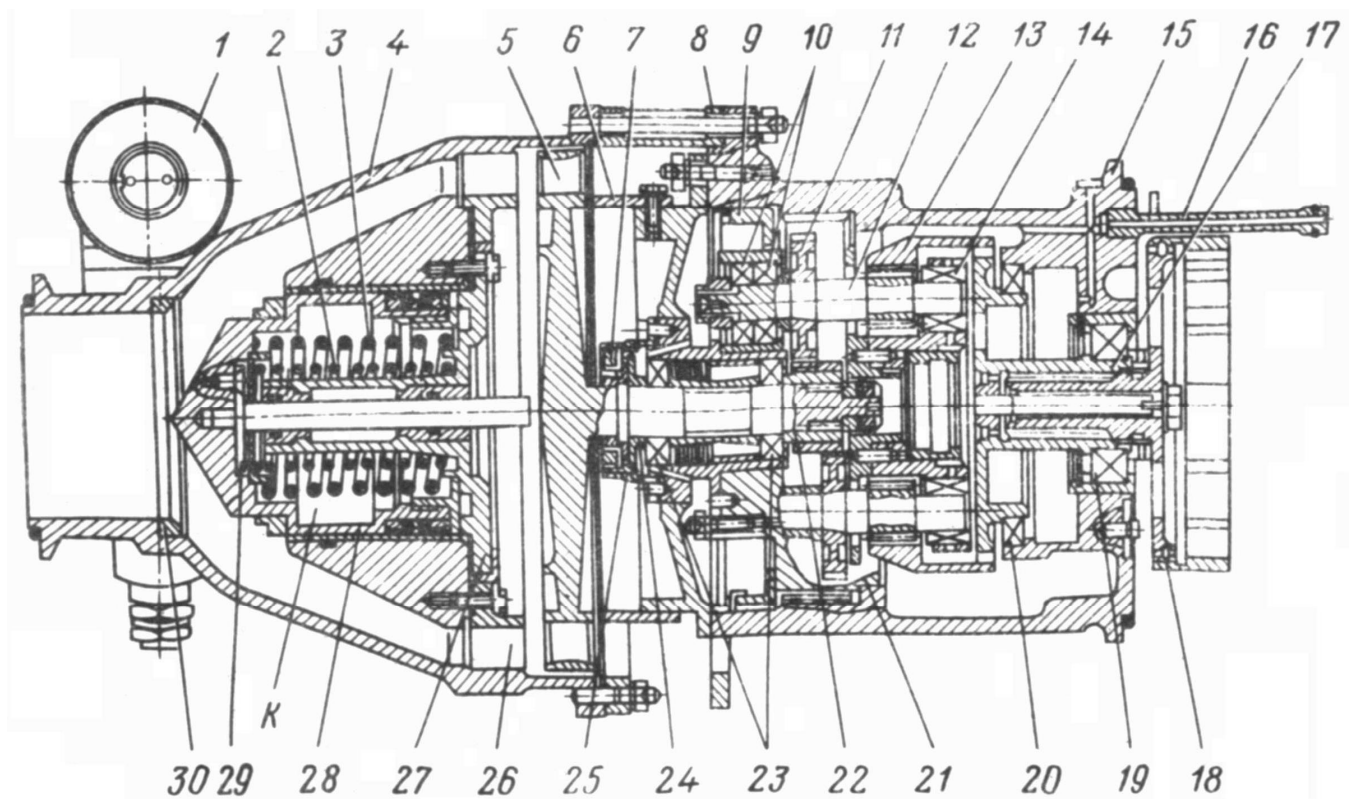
Конструктивная схема воздушного турбостартера СтВ-3: 1 – электромагнит ЭМТ-707; 2, 3 – пружины; 4 – корпус заслонки; 5 – ротор турбины; 6 – разрезной кожух; 7 – втулка; 8 – корпус; 9 – гайка; 10 – шарикоподшипник; 11,13 – шестерни; 12 – валик-шестерня; 14 – подшипник игольчатый; 15 – корпус редуктора; 16 – трубка подвода масла; 17 – муфта; 18 – опора храповой муфты; 19, 20, 23 – шарикоподшипники; 21 – корпус перебора; 22 – ведущая шестерня; 24 – упор; 25 – уплотнение графитовое; 26 – сопловой аппарат; 27 – опора; 28 – плунжер; 29 – шток; 30 – седло
